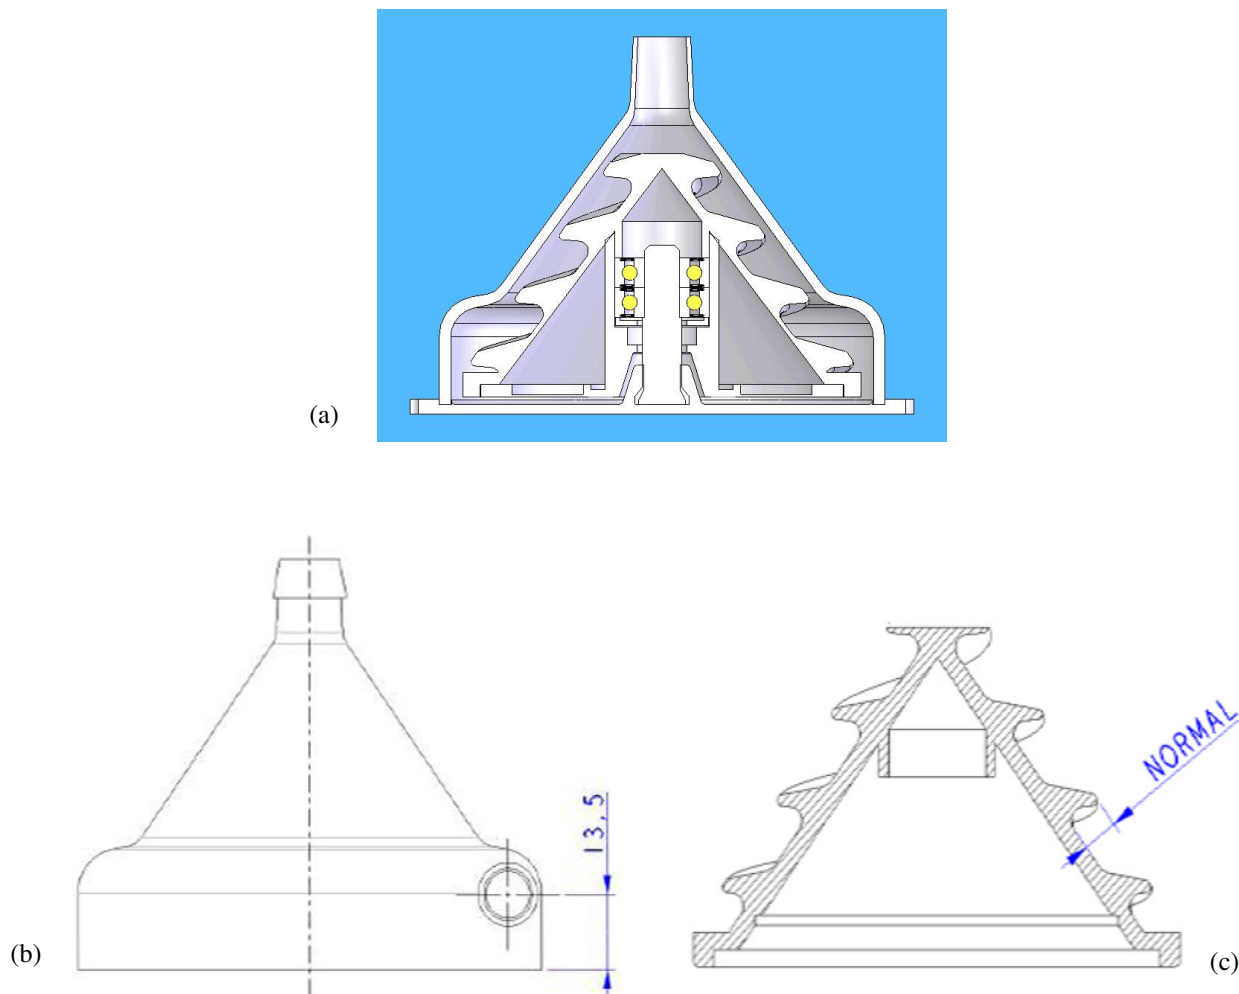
(a) Desenho esquemático do Protótipo 1, (b) desenho técnico do cone externo e (c) desenho técnico do rotor.
